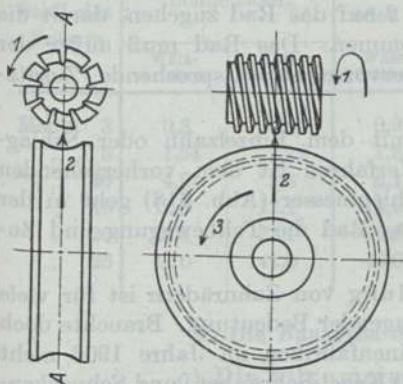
und 615. Fräsen der Schneckenräder mit zylindrischem Fräser.
